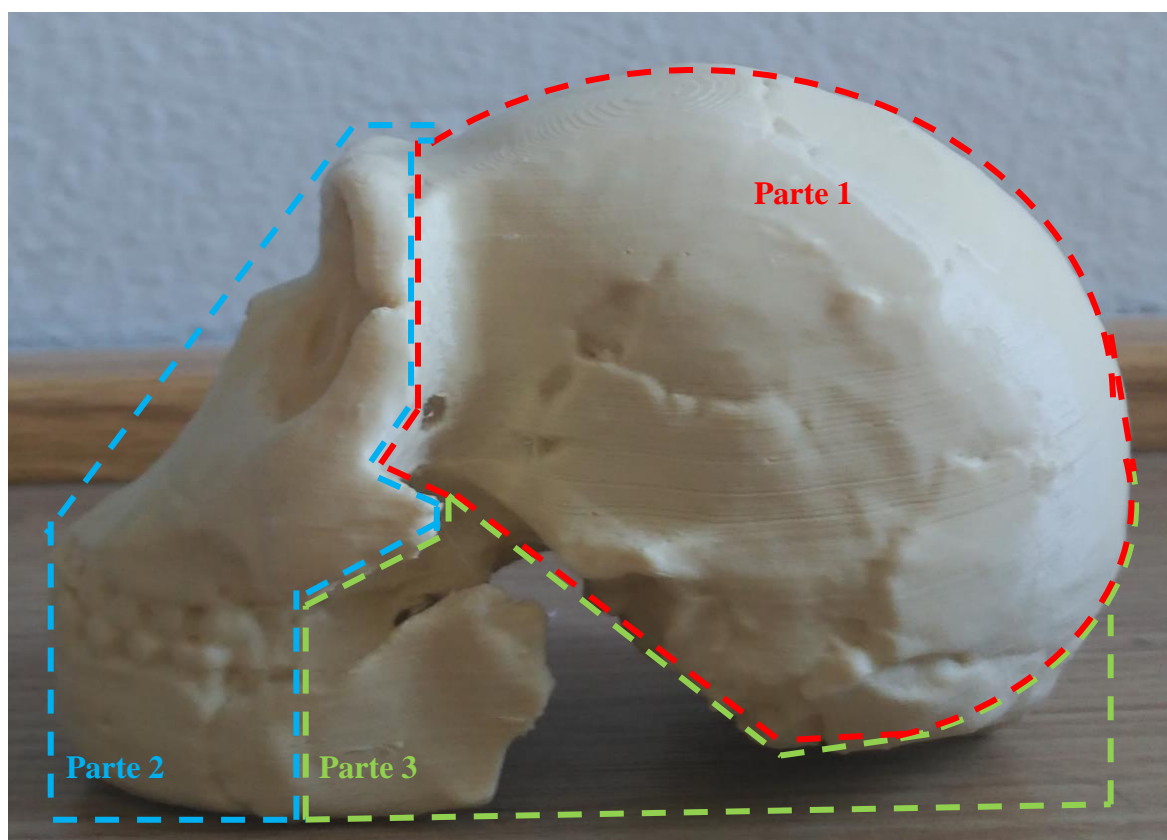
Configuración del molde en 3 piezas diferentes. ©María Ávila Rodríguez.
